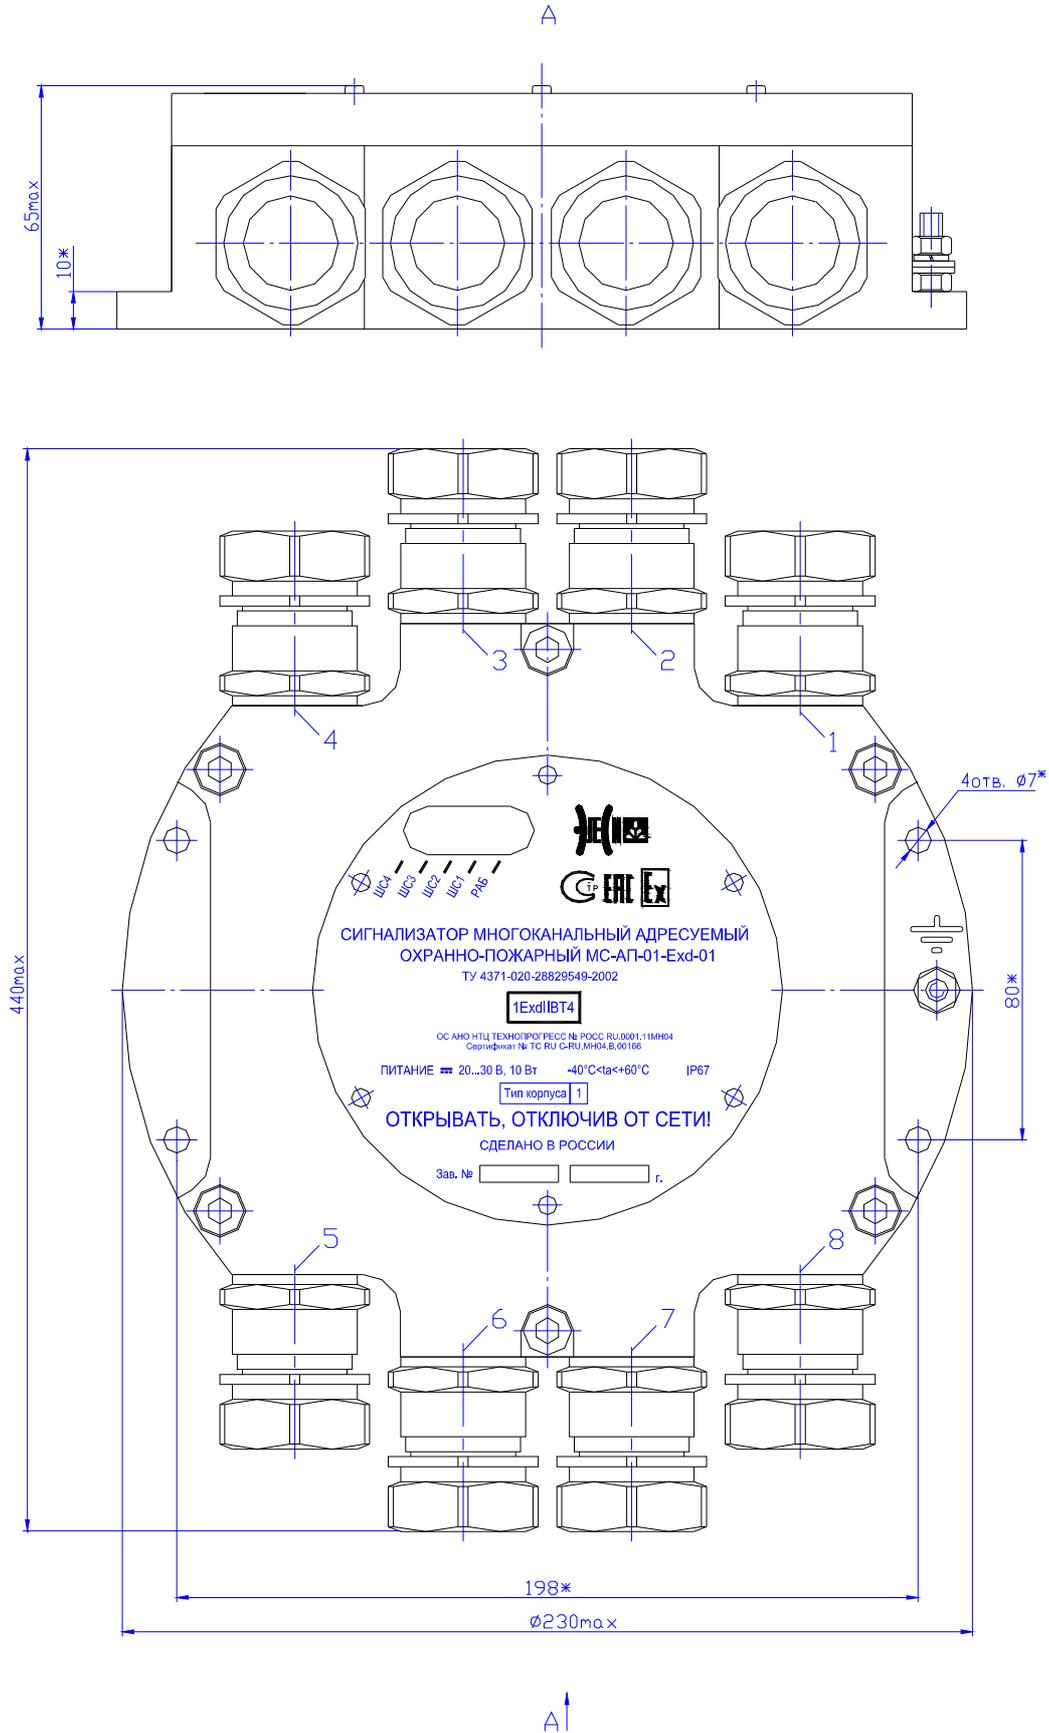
Габаритный чертеж исполнения МС-АП-01-IP
